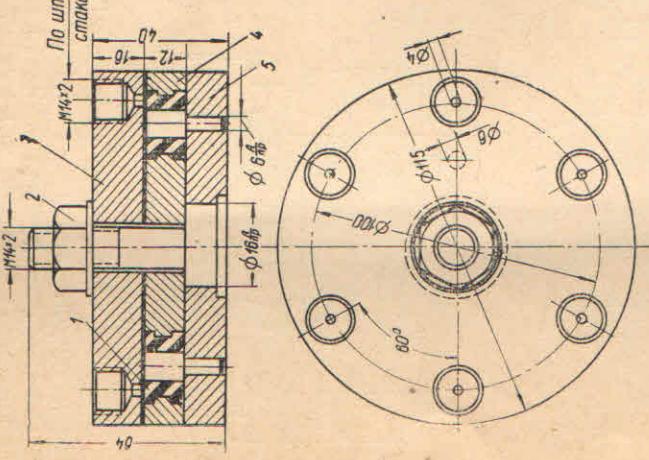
Пресс-форма в сборе с деталью № 20-1703045 — подушка противовеса рычагов передней подвески.
